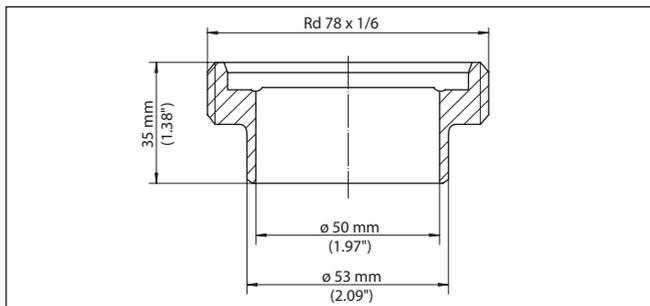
Medidas da luva para soldagem união roscada para tubo DN 50 (DIN 11864-1)
